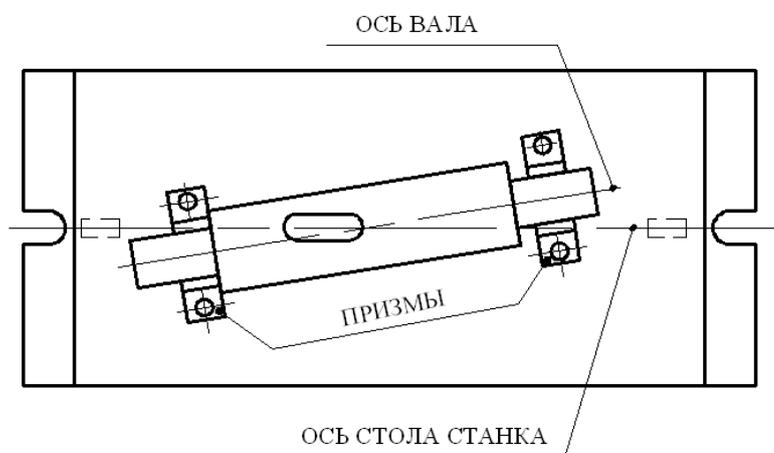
Возникновение погрешности установки приспособления на станке
